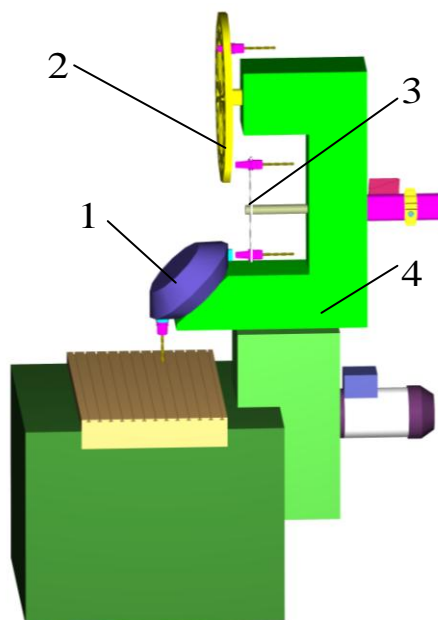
Схема комбинированного устройства АСИ: 1- револьверная головка; 2 – магазин; 3 – манипулятор; 4 – шпиндельная бабка
